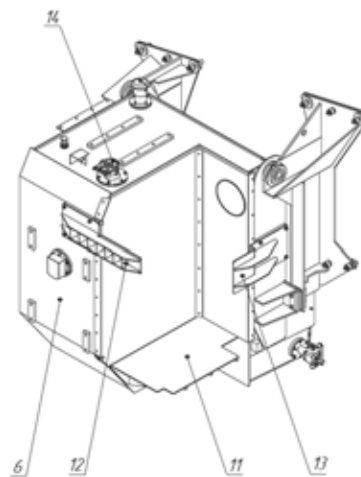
Модернизированный стандартный дизельный топливный бак: 6 – модернизированный стандартный дизельный топливный бак; 11 – технологическая ниша; 12, 13 – ограничители; 14 – заливная горловина /
